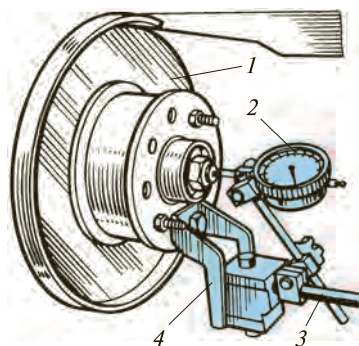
Проверка осевого зазора подшипника ступицы переднего колеса:
